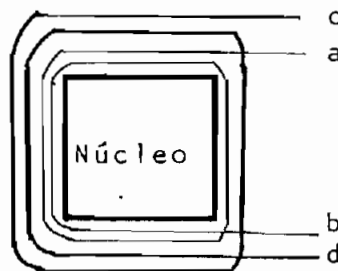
Vista frontal de la saliente del estator con la disposición física de las bobinas.
